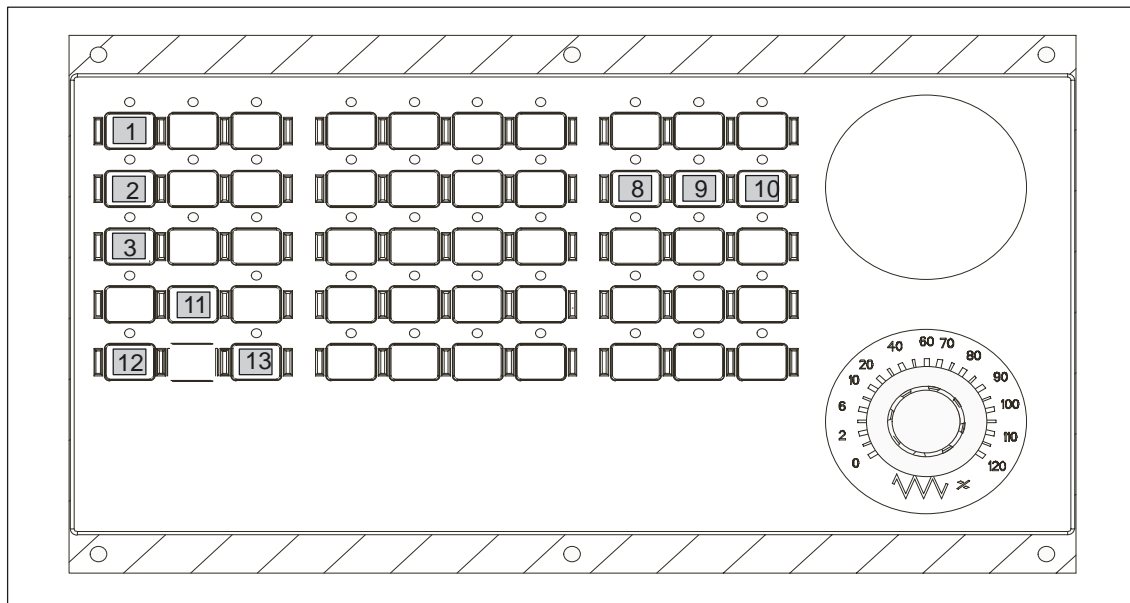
Tastenbelegung Maschinensteuertafel für OP032S
